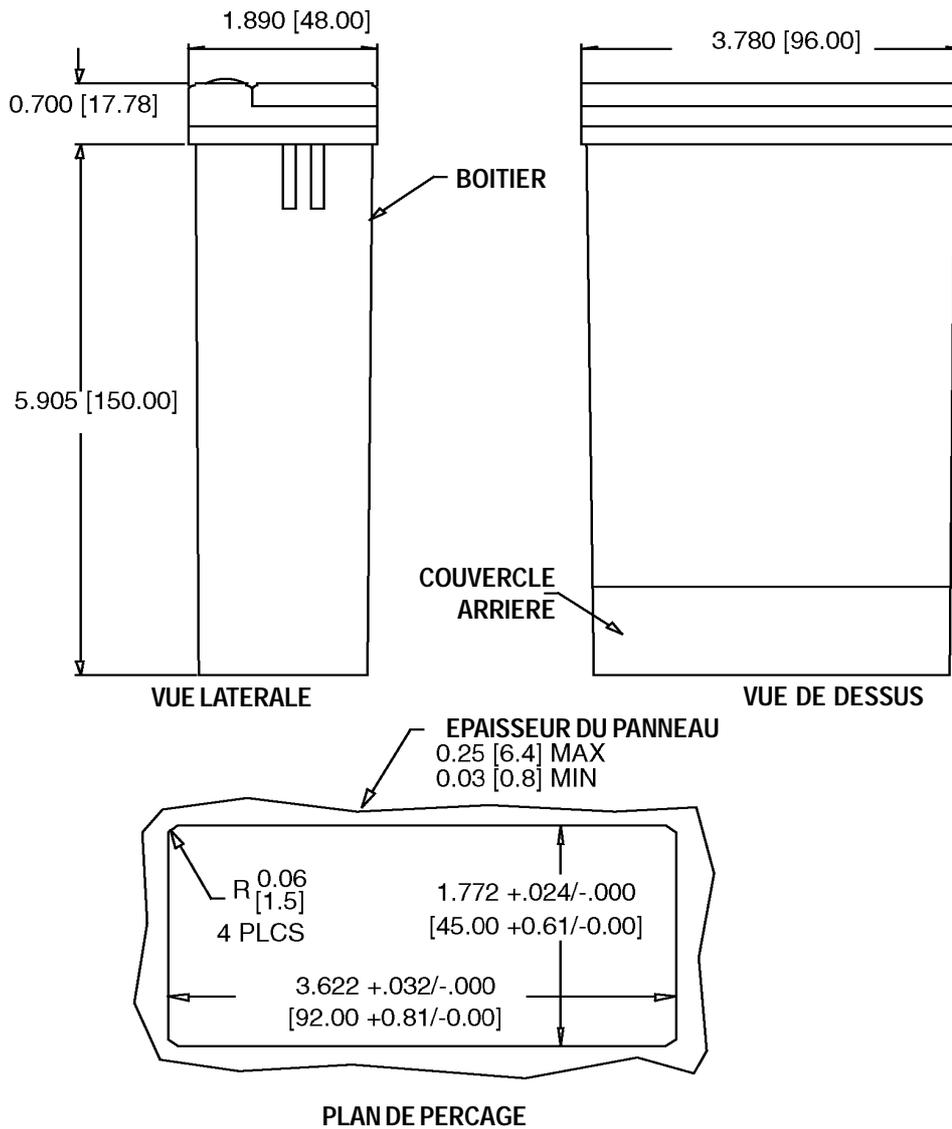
Dimensions du boîtier et Plan de perçage
